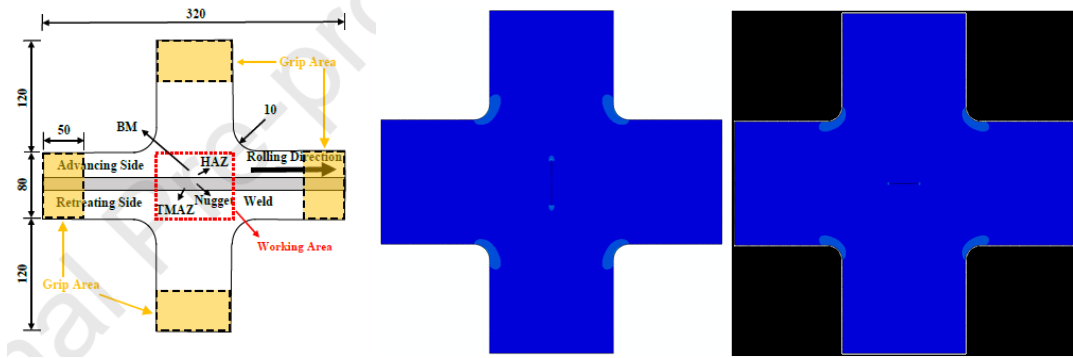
8 :Joint cruciforme a) position du joint de soudure b) fissure perpendiculaire c) fissure transversale
